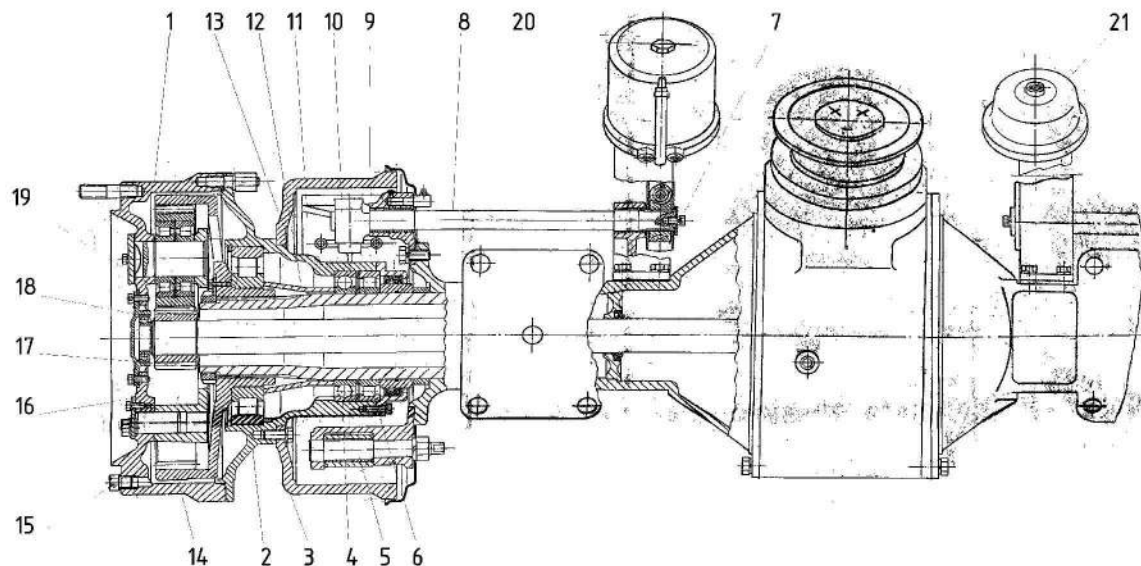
Задний мост трактора К-744Р2 с конечной передачей: 1 – водило; 2, 6 – цилиндрический роликоподшипник; 3 – ступица; 4 – шарикоподшипник; 5 – эксцентриковая ось; 7 – рычаг тормоза; 8 – суппорт; 9 – асбофрикционная накладка; 10 – кулак; 11 – тормозная колодка; 12 – труба; 13 – тормозной барабан; 14 – вечная шестерня; 15 – шестерня-сателлит; 16 – крышка; 17 – солнечная шестерня; 18 – шарикоподшипник; 19 – полуось; 20 – тормозная камера с пружинным энергоаккумулятором; 21 – тормозная камера.
